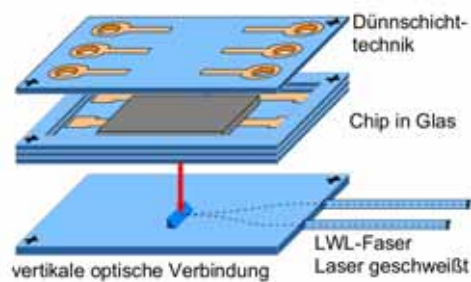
glassPack-Konzept für Sensoren und High-Speed-Module
